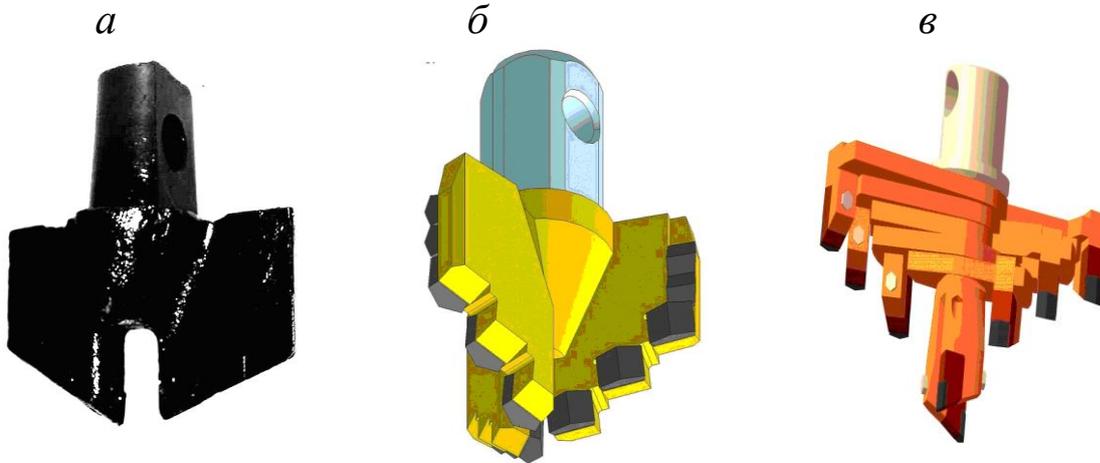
Режущий буровой инструмент: а – со сплошной кромкой; б – со ступенчатой кромкой; в – с резцами
